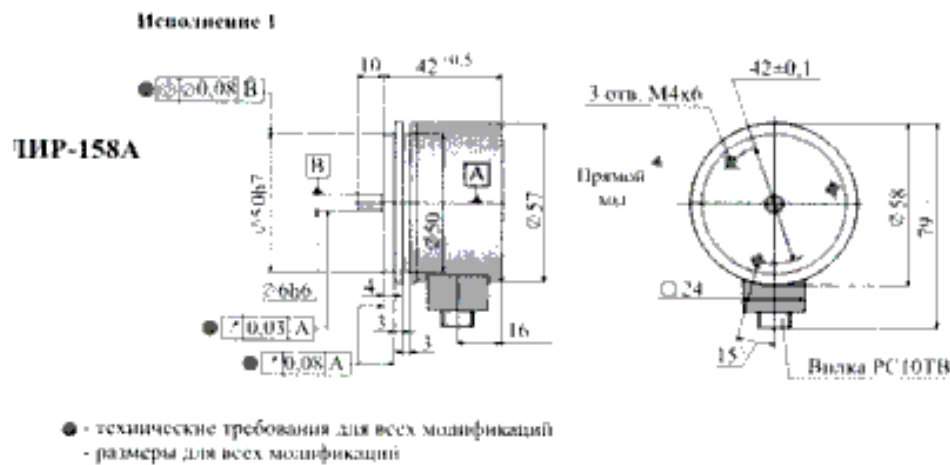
Габаритный чертеж датчика ЛИР-158
